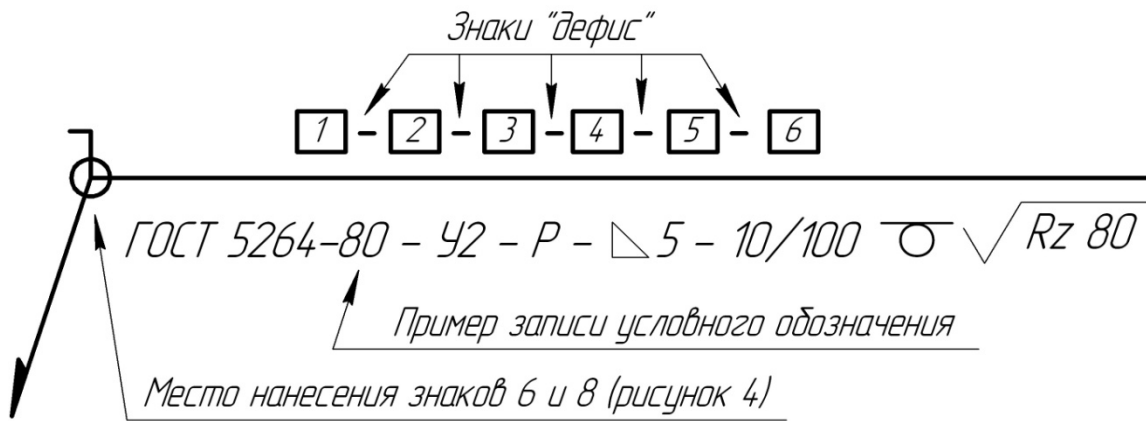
Структура условного обозначения стандартного сварного шва
